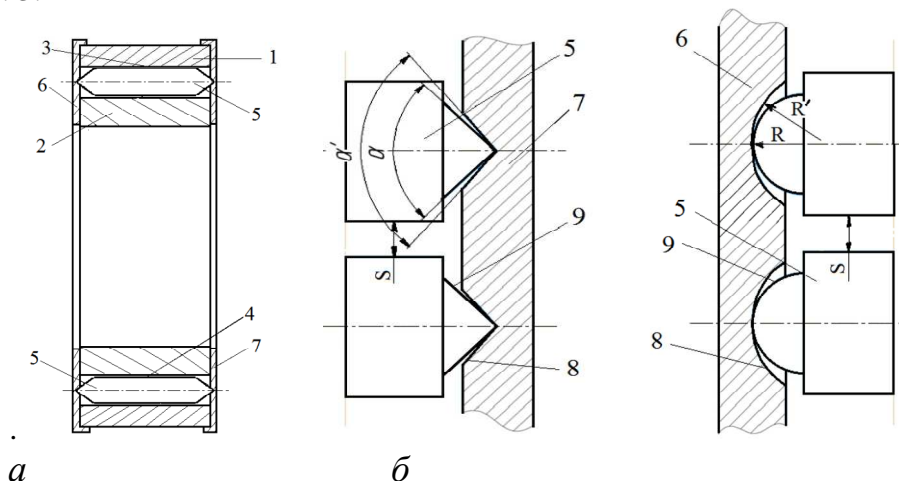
Схема подшипника качения и контактов тел качения: а – вид подшипника в сечении; а – схема конических поверхностей контакта тела качения и выемки правой торцевой крышки (конусообразная форма); б – схема конических торцевых поверхностей контакта; в – схема сферических торцевых поверхностей контакта тела качения и выемки левой торцевой крышки (сферическая форма)
